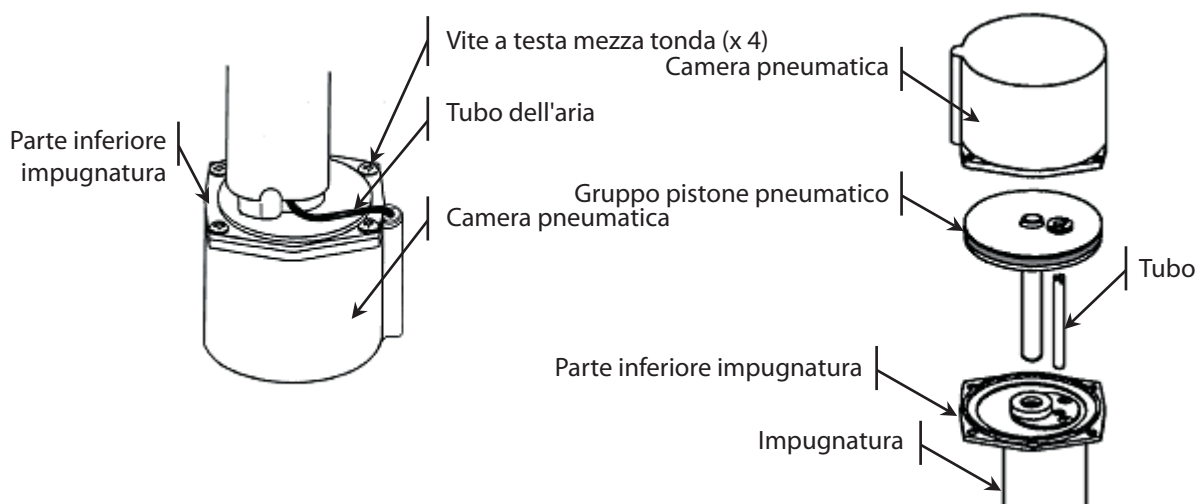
Rimozione della camera pneumatica e del gruppo del pistone pneumatico
